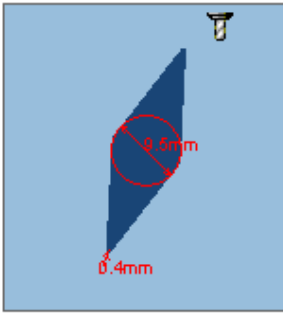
Ріжуча пластинка «VBMT 16 04 04-UM 4425»
